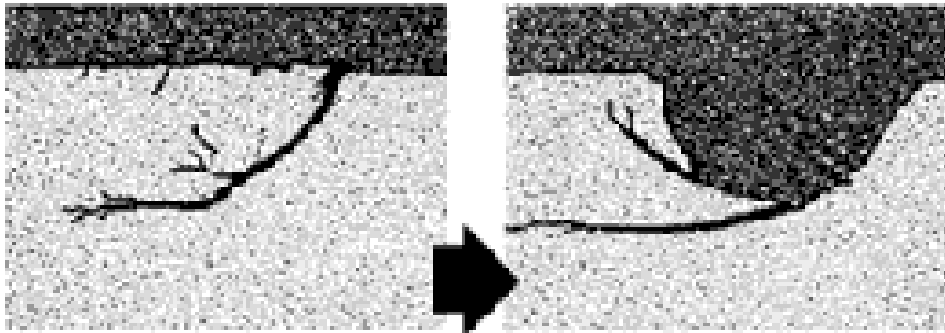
Propagación de grietas por debajo de la superficie
